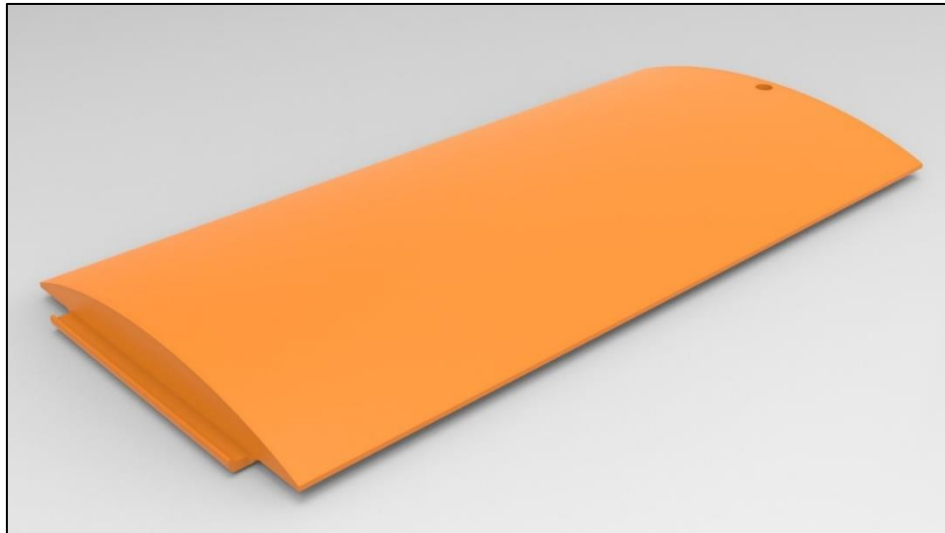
Tapa del fuselaje - vista isométrica [Autores].
